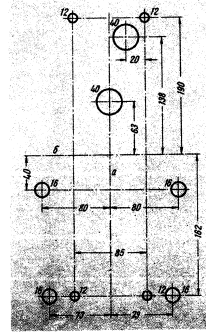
Сверление отверстий для установки на изоляционных плитах контакторов типа КП 505 и КП 515, с задним присоединением
